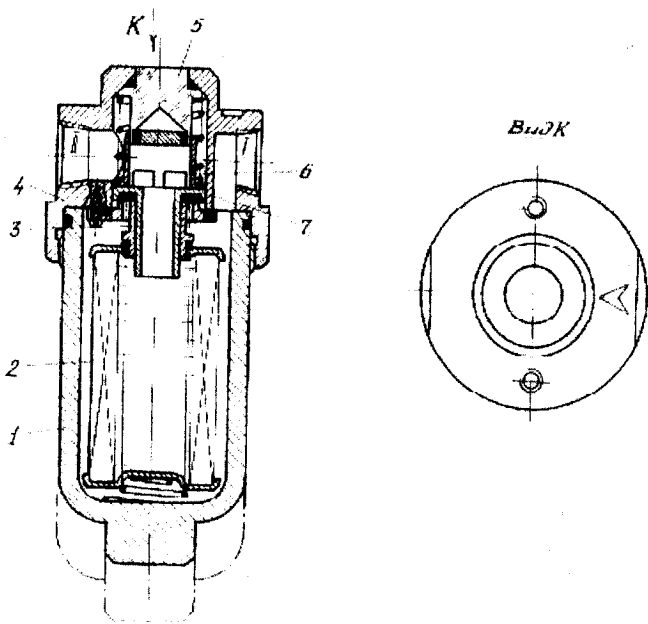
Конструкція напірного фільтра типу Ф-10
